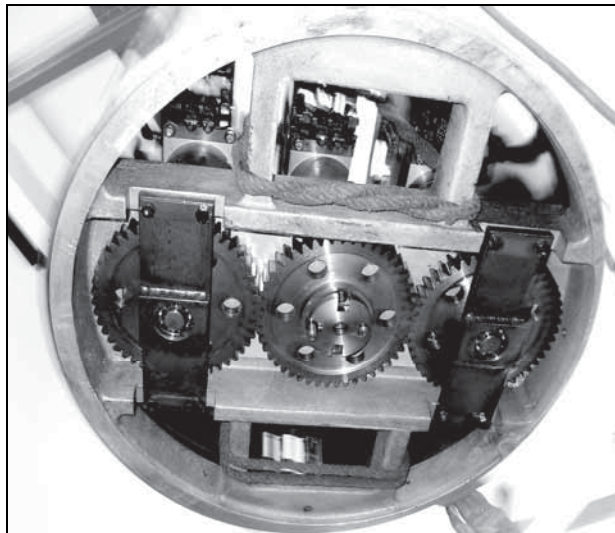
Внешний вид нижней торцевой части приводного механизма контактора РПН типа SDV (приведённого на Рис. 1.28).
